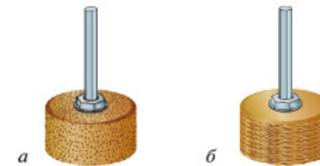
Насадки для дрели: а — для чистовой обработки и шлифования заготовок; б — войлочная насадка для полирования
